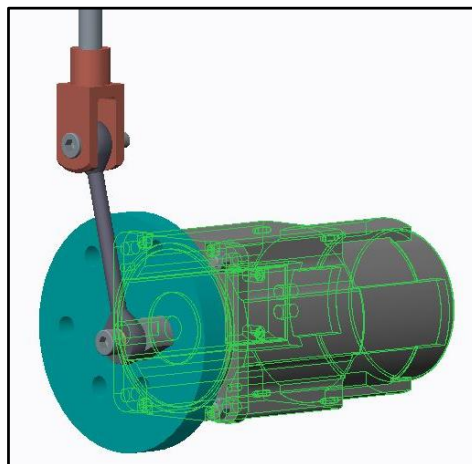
6. Visualización del motor en la máquina de ensayos unido al eje de la excéntrica.
